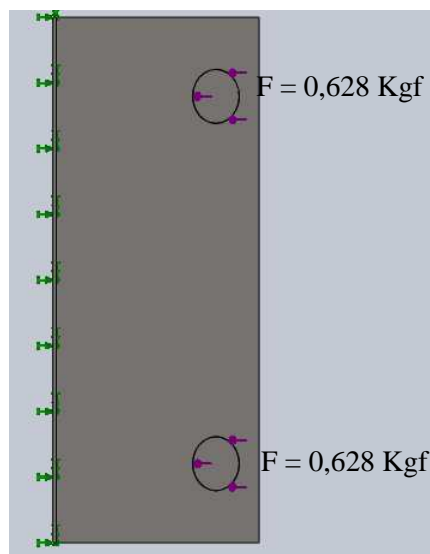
Cargas aplicadas en la platina de centrado exterior
